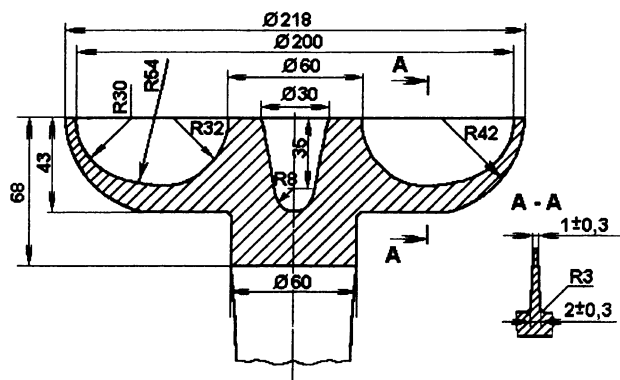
Конструкция отливки "Рабочее колесо гидромолоты"
